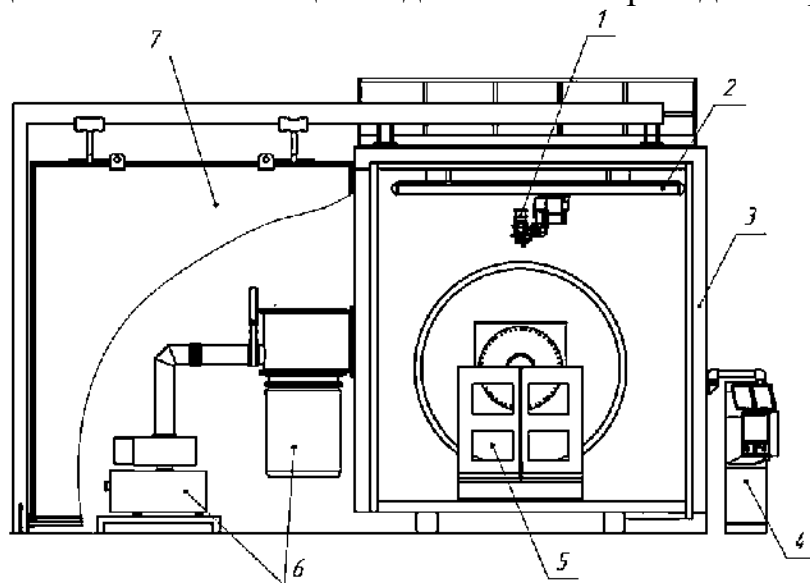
Общий вид опытного образца установки АЭЛТК-135-455:
